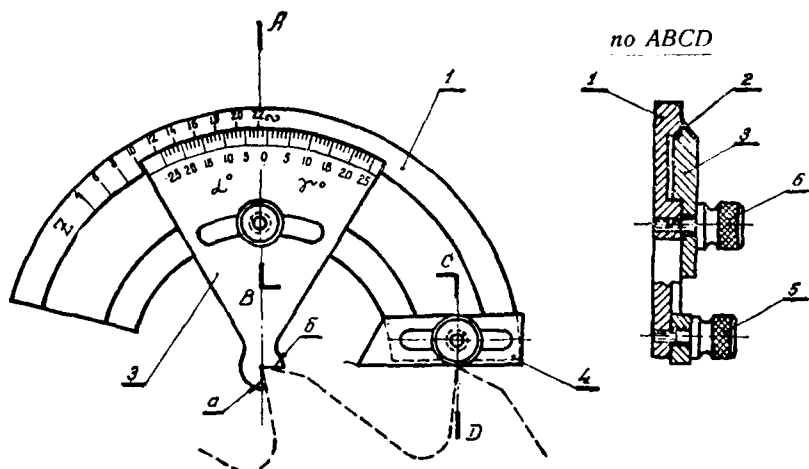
Угломер для измерения переднего и заднего углов фрез
